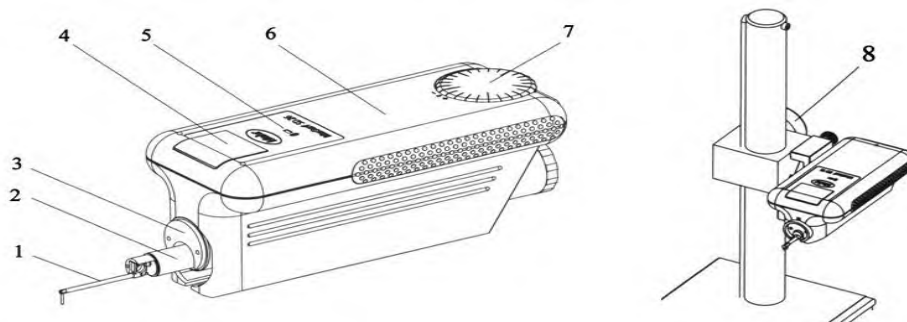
Схема профилометра MarSuf SD 26: 1) консоль щупа; 2) датчик, интегрированный в механизм подачи и оснащенный магнитным фиксатором для консоли щупа; 3) механизм подачи; 4) кнопка запуска (Старт); 5) индикатор статуса Bluetooth-соединения; 6) корпус прибора; 7) маховик для регулировки угла наклона; и 8) рукоятка для настройки высоты [7].
